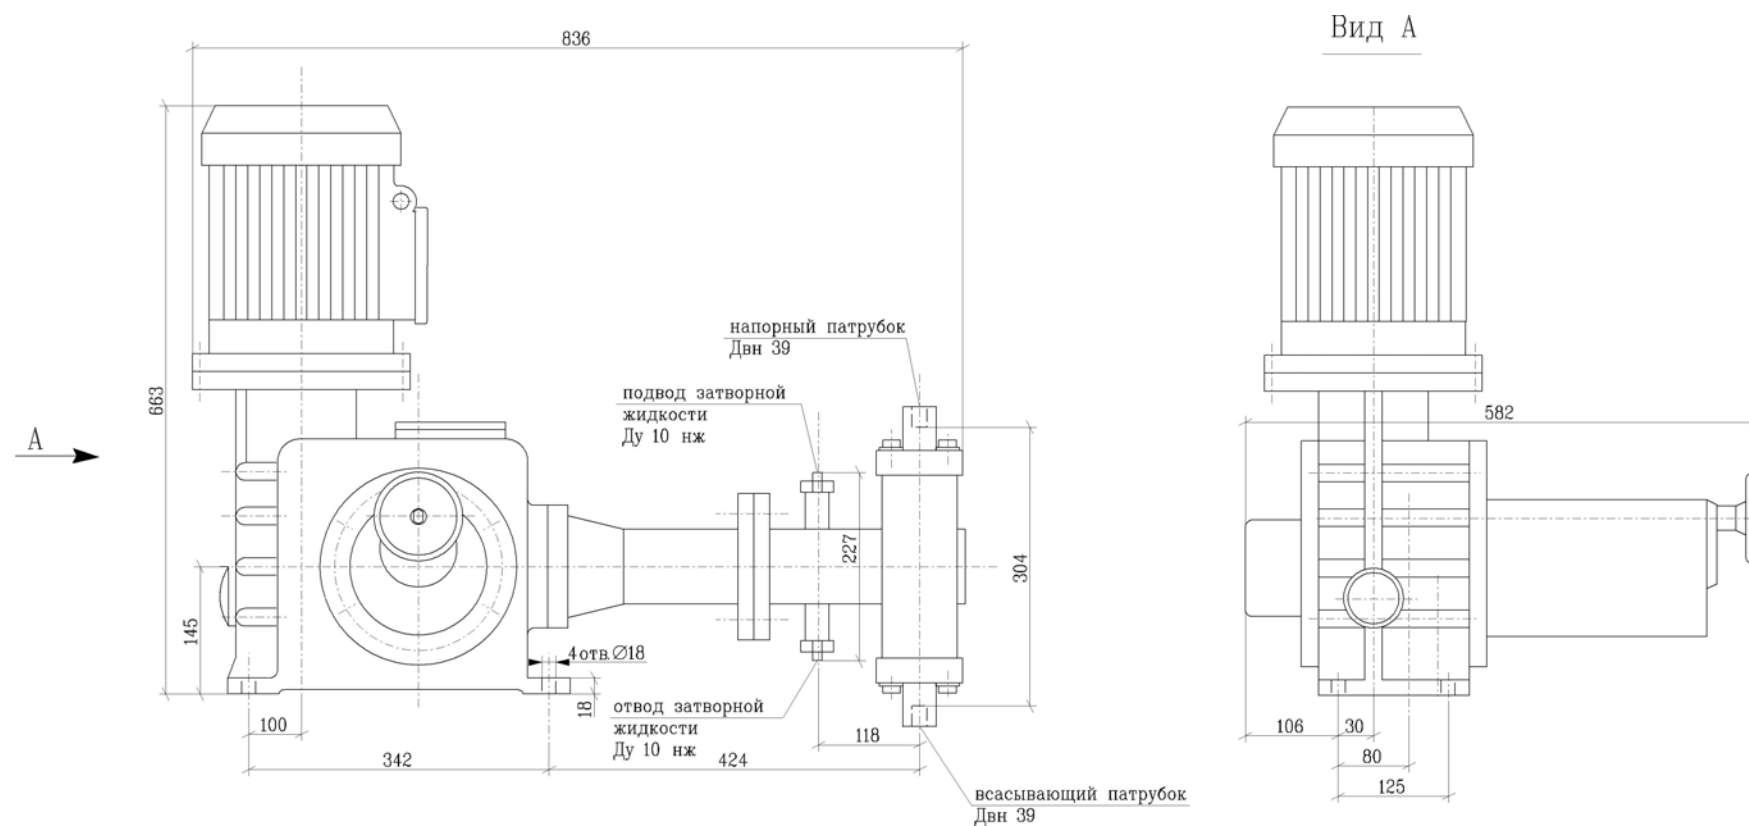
Габаритный чертеж насоса-дозатора щелочи LDB60AP001, LDB60AP002
